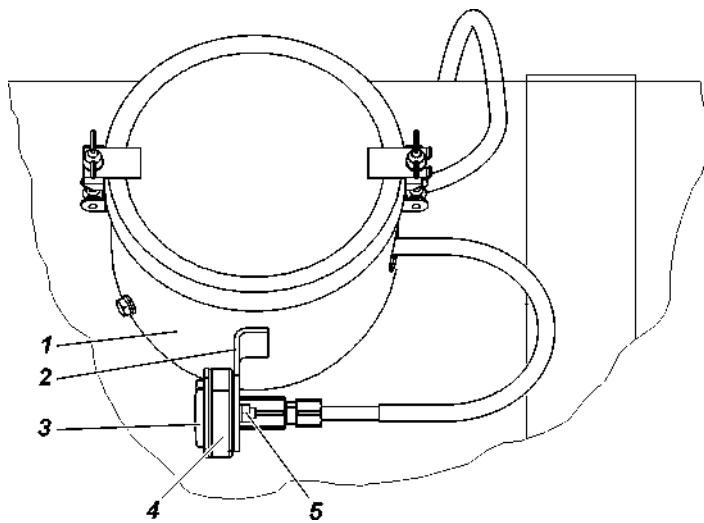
Установка заправочного устройства с продольным расположением баллона::
